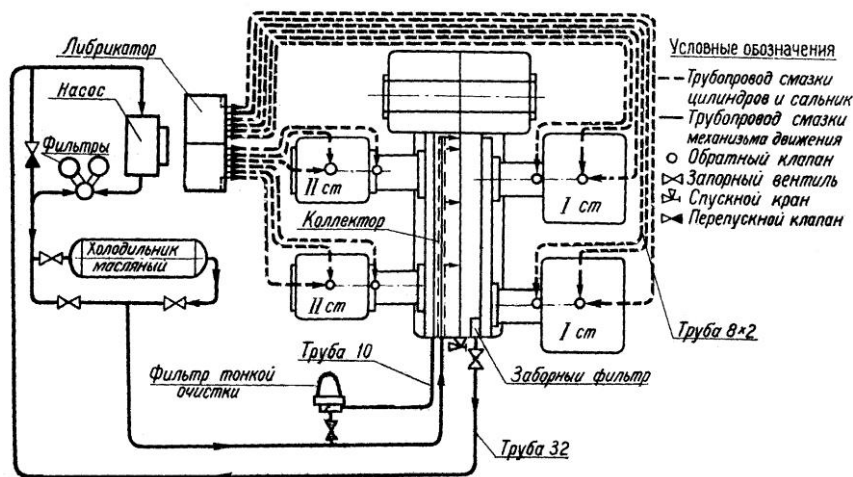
Система смазки оппозитного компрессора 4М10 – 100/8
